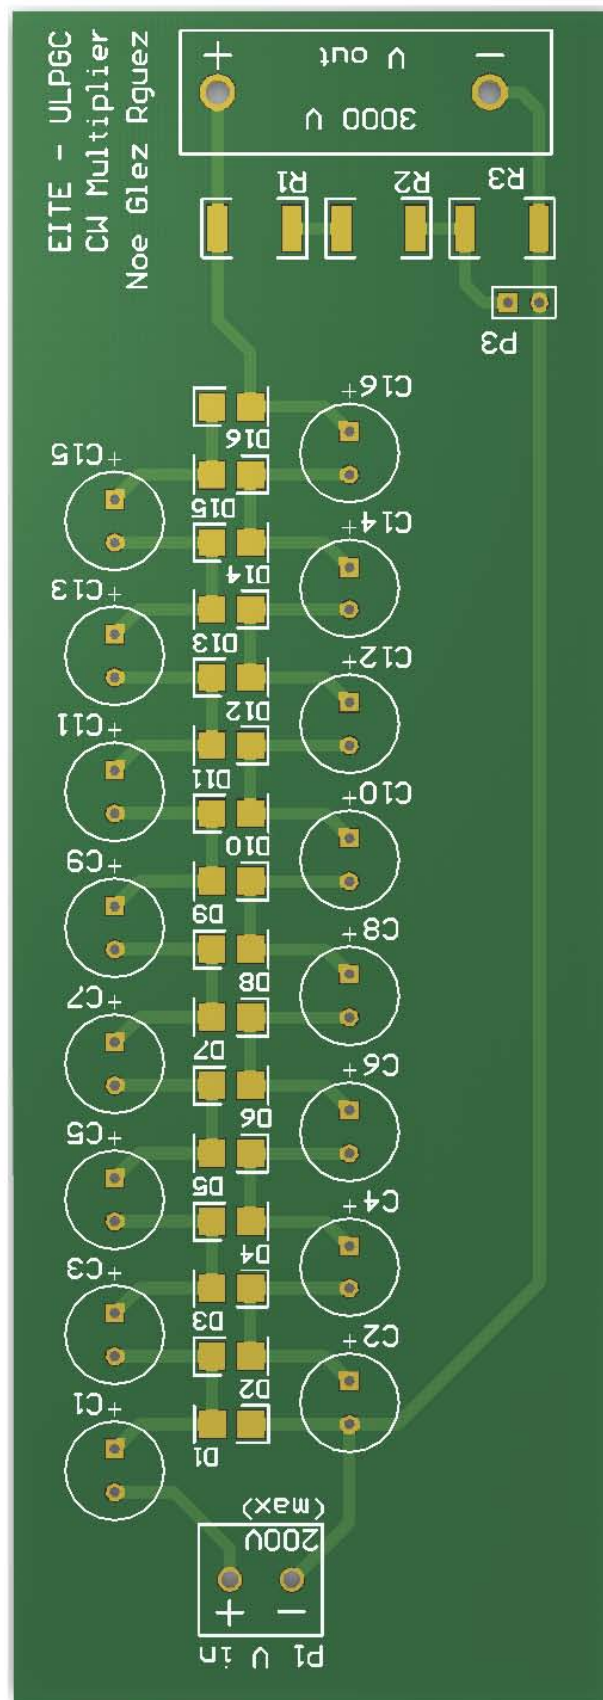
Layout del circuito multiplicador en PCB. Vista virtual.
